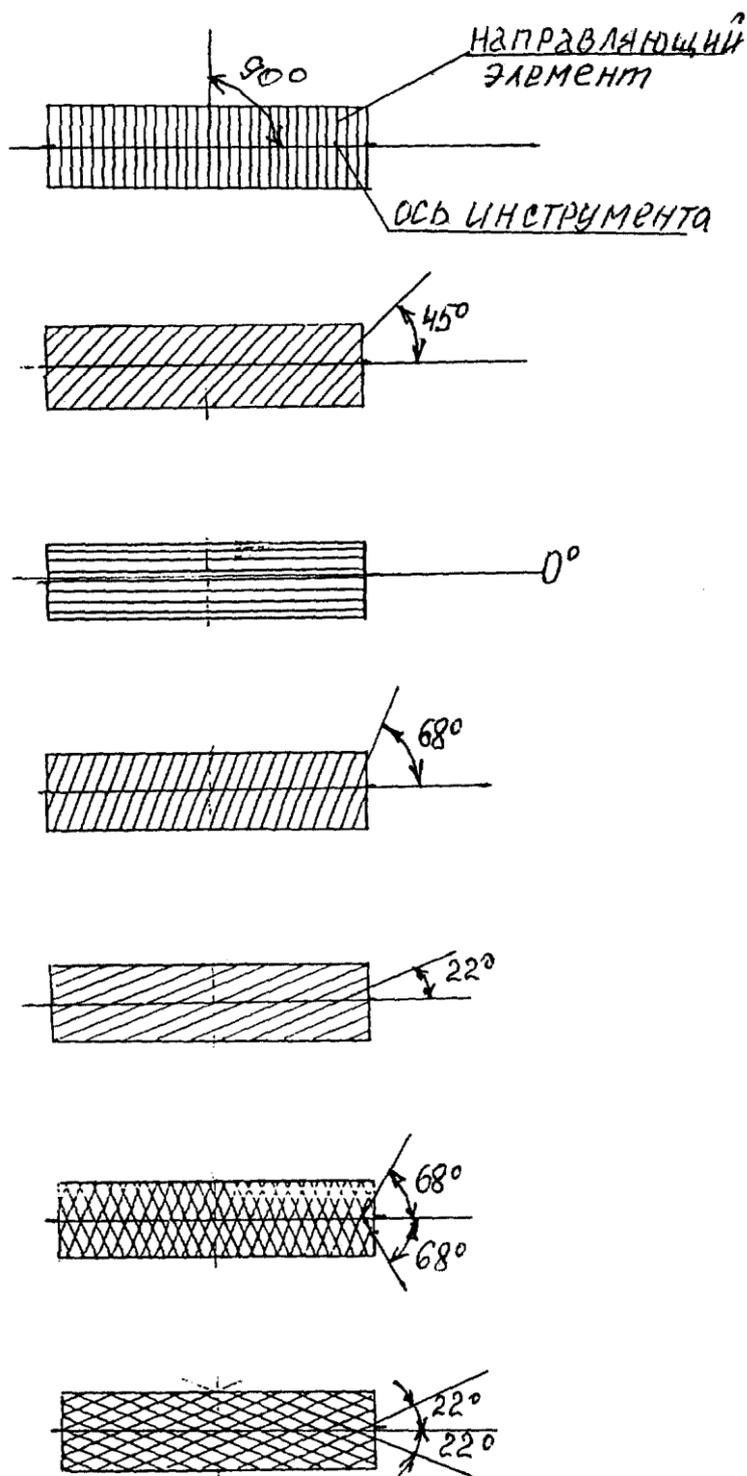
Расположение микронеровностей на поверхности направляющей пластины
